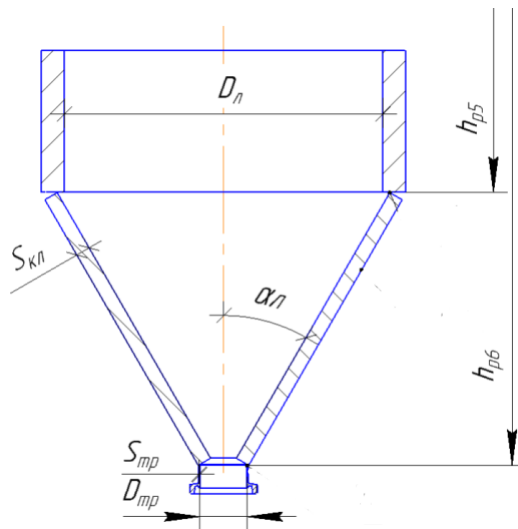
Перехід з циліндричної обичайки на нижньою конічною частиною.
